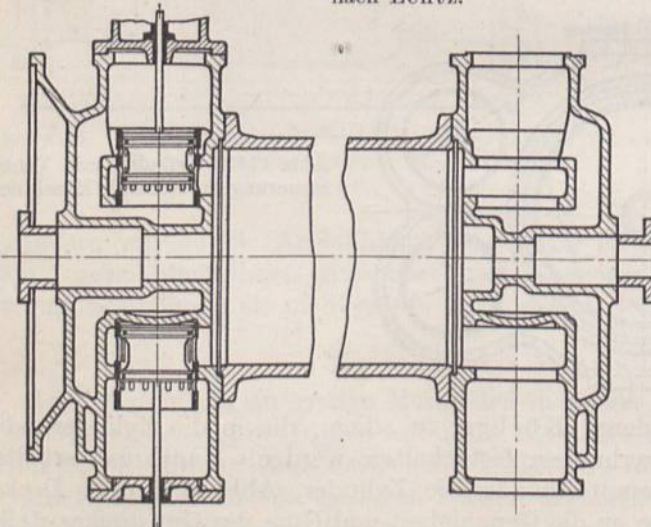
Zylinder mit Kolbenventilsteuerung.
